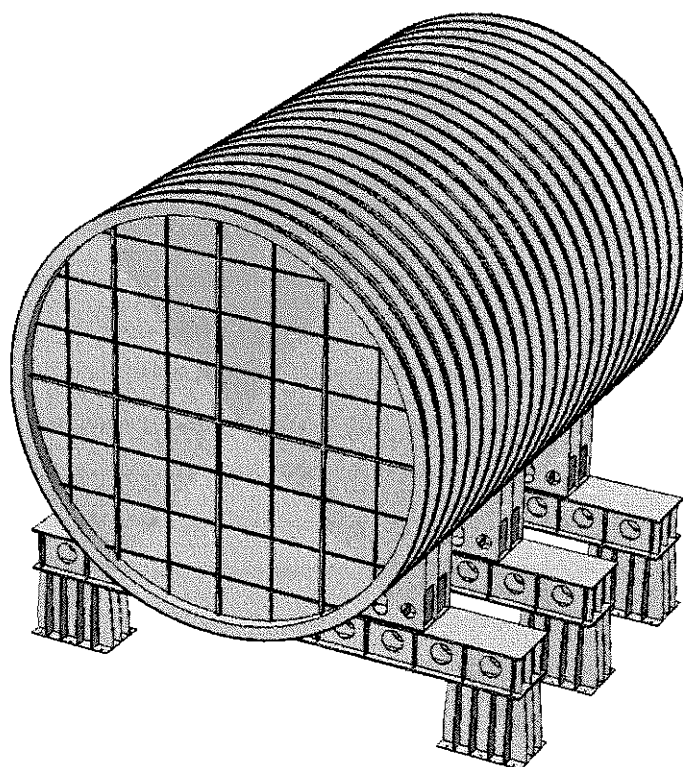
Постановка блока РО на трёх опорных фундаментах с опорными балками
